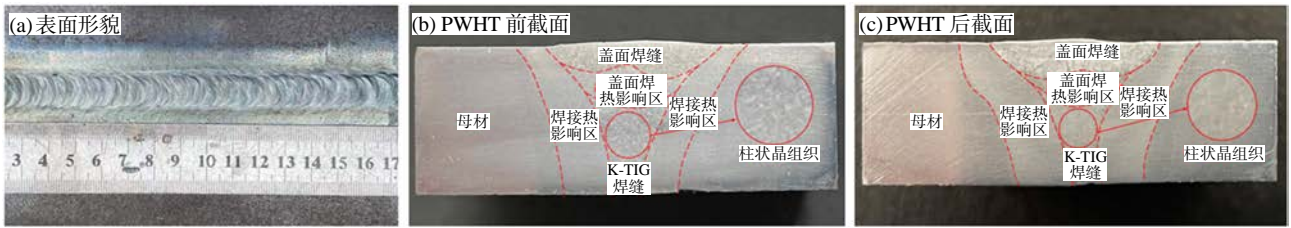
盖面焊后的焊接接头表面和截面形貌
